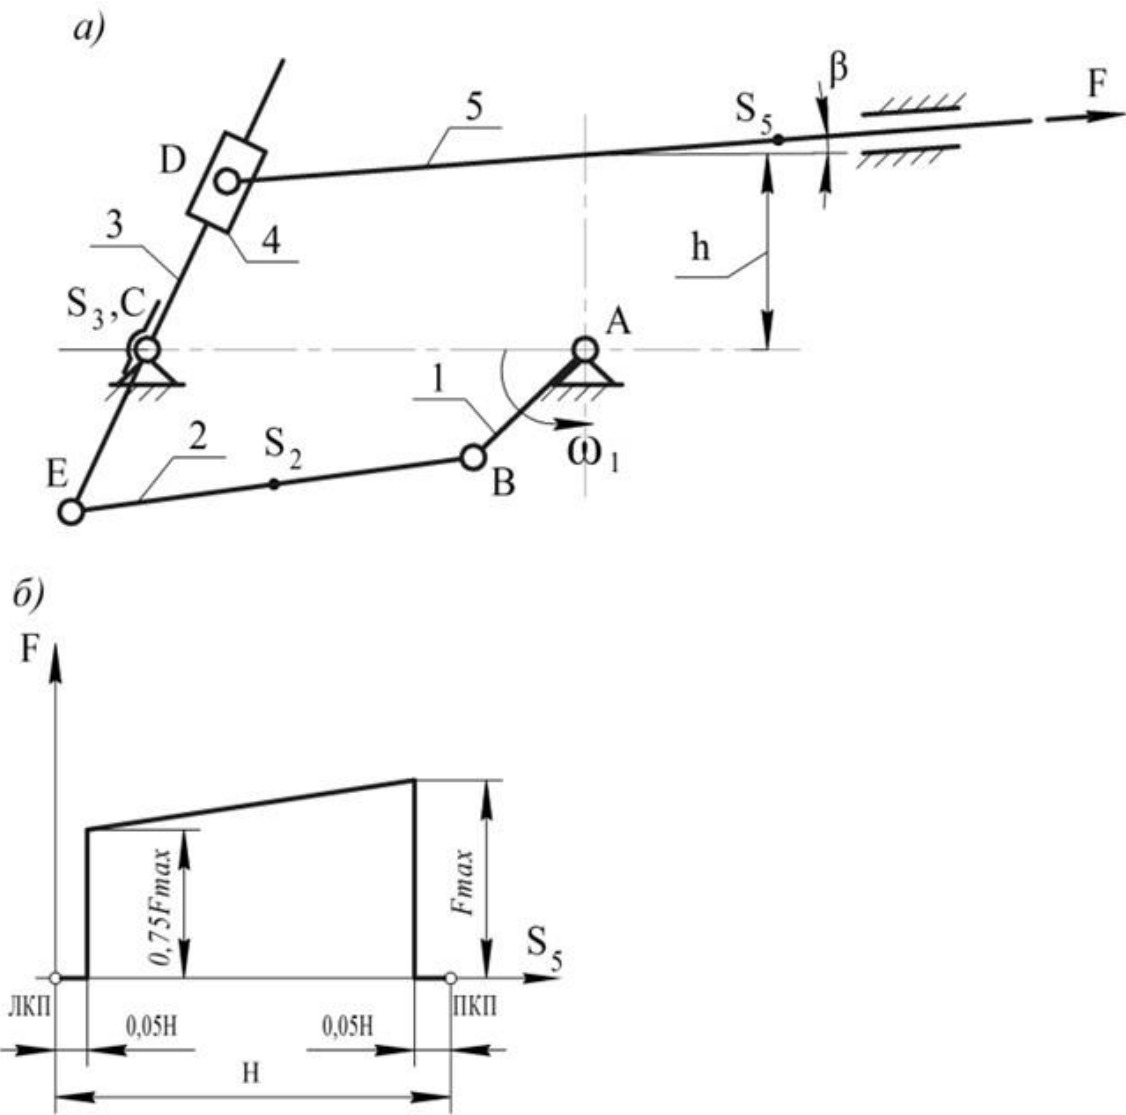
Схема рычажного механизма станка для нарезания конических колес с прямым зубом
